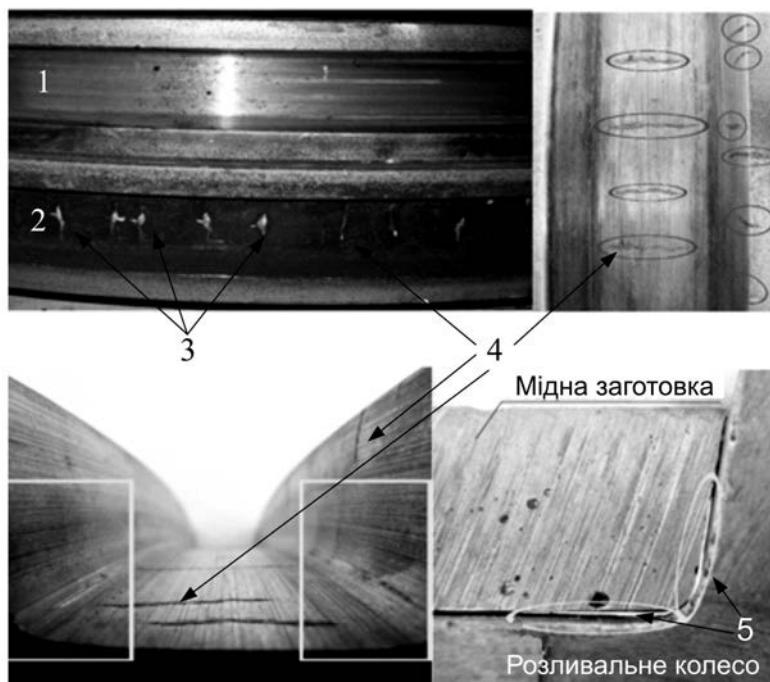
Дефекти робочої поверхні розливальних коліс: 1, 2 – відпрацьовані колеса; 3 – фрагменти мідної безперервнолитої заготовки; 4 – тріщини на робочій поверхні колеса; 5 – деформація профілю колеса в кутах робочого каналу.
